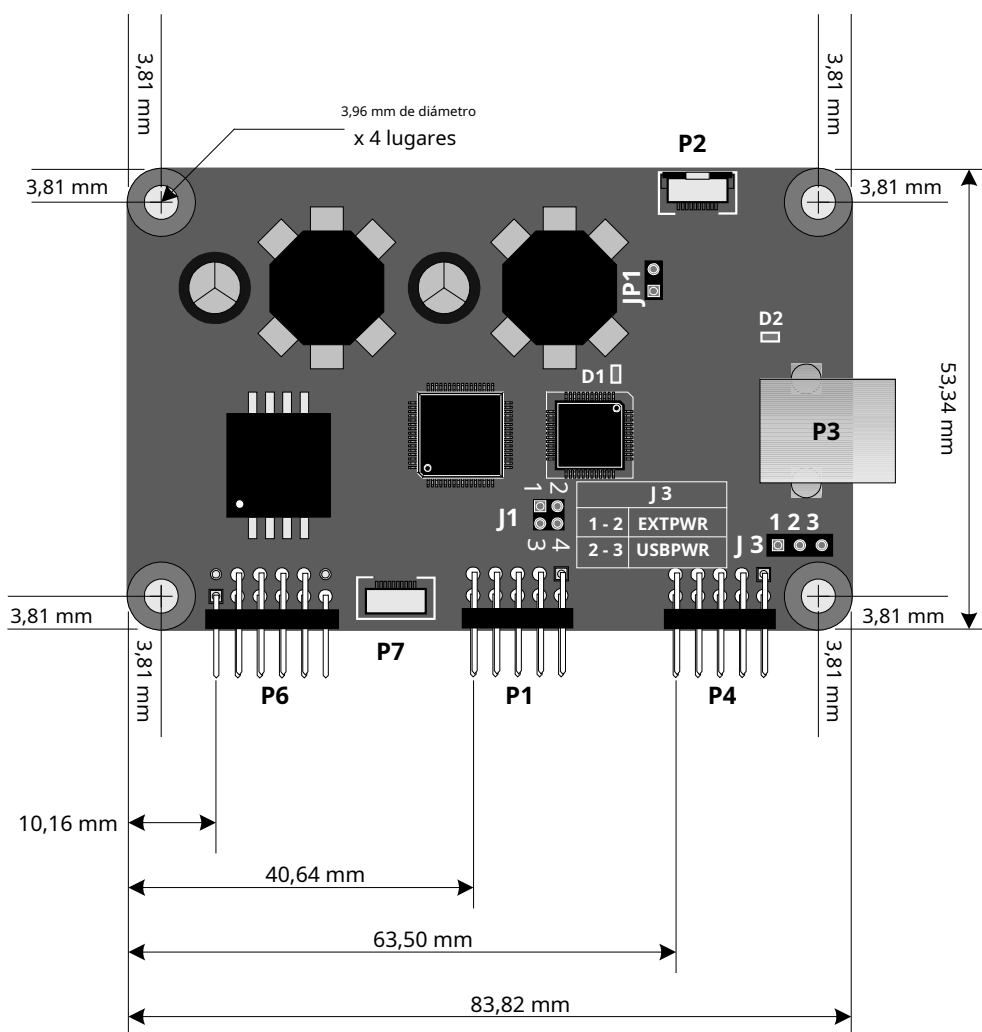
2521 Dimensiones (CTR-252100-IT-USB-00-R)
